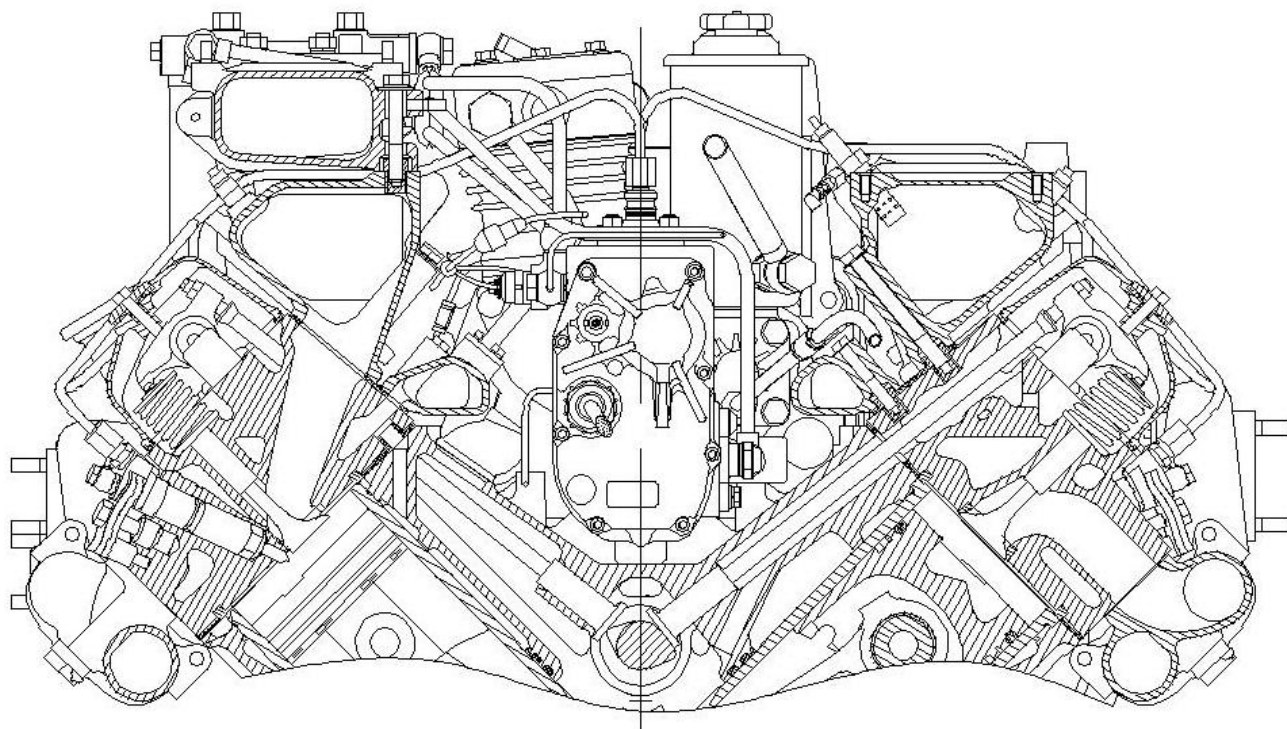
Поперечный разрез двигателя с рядным ТНВД «БОШ»
